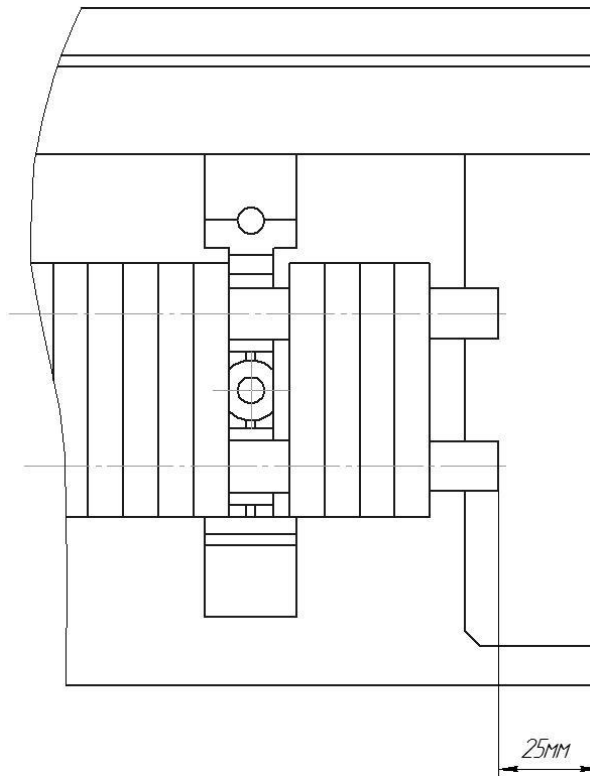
Для установки з'єднувача кінцевого СК.
